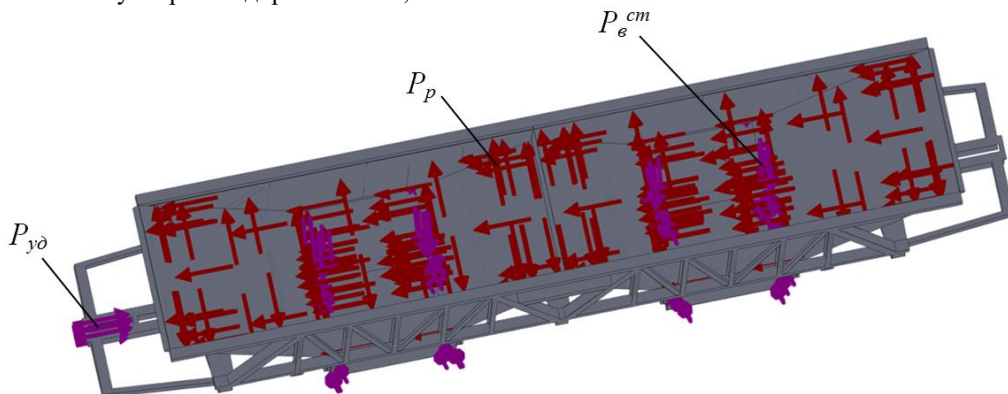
Розрахункова схема несучої конструкції вагона-хопера
